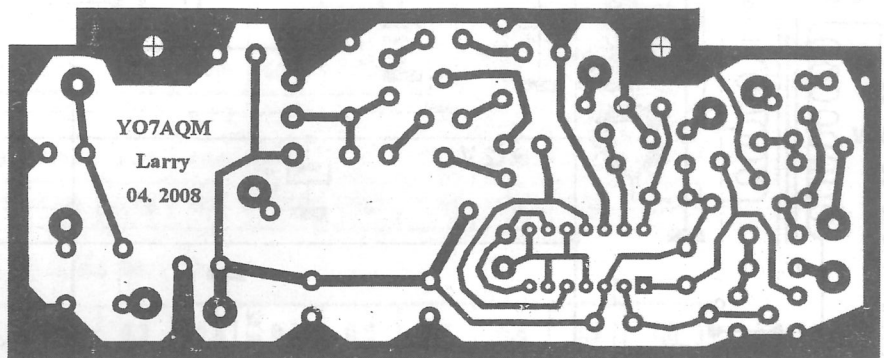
Placa 1; desenul cablajului, vedere dinspre fața placată (115 x 47 mm).
